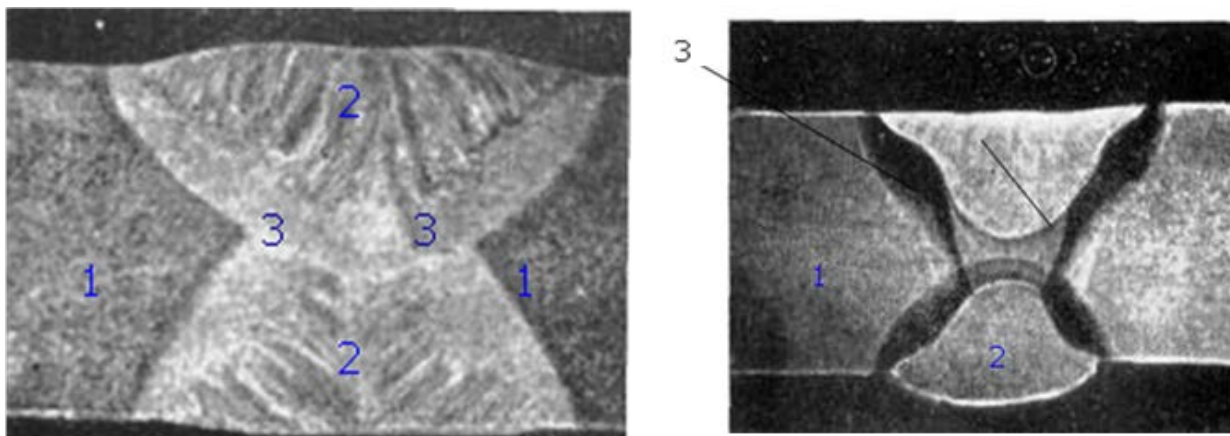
Будова зварного шву: 1 – основний метал, 2 метал шву, 3 – метал зони термічного впливу (зтв)
